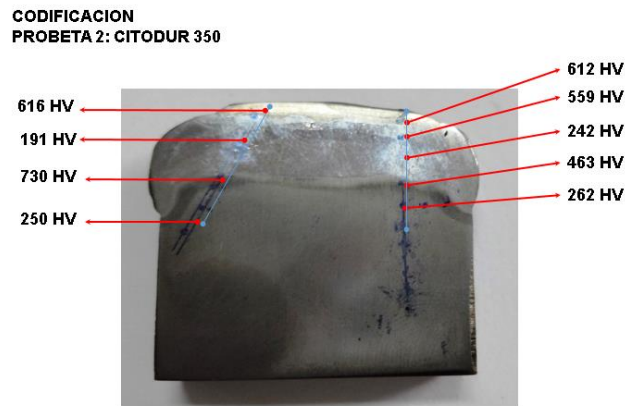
Probeta soldada con electrodo Citodur 350
